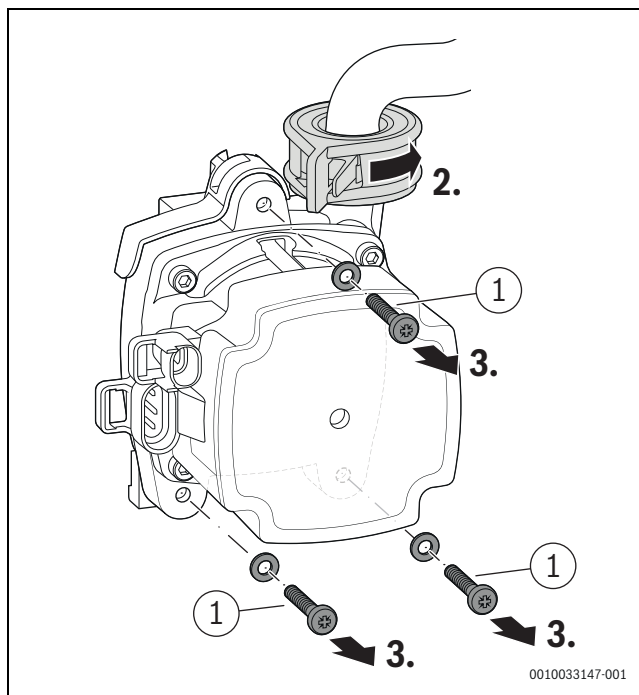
Déverrouiller la pompe de chaudière et retirer les vis
